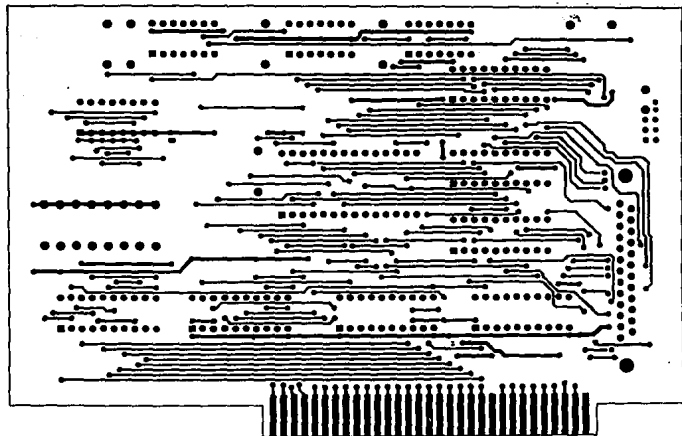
Circuito impreso de la tarjeta simulador de ROM lado de componentes
